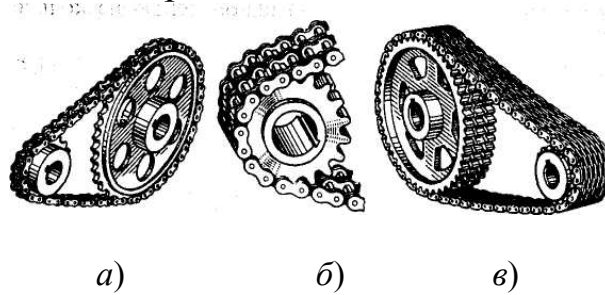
Типы цепных передач: а – с роликовой цепью; б – с втулочной цепью; в – с зубчатой цепью
